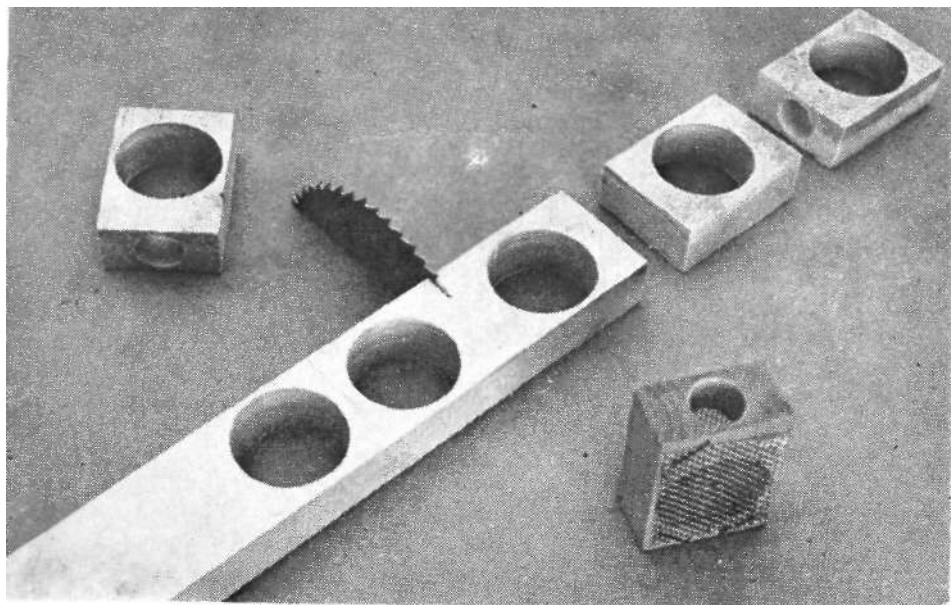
Клеточки для выщипления маток изготавливают из бруска мягкой древесины
